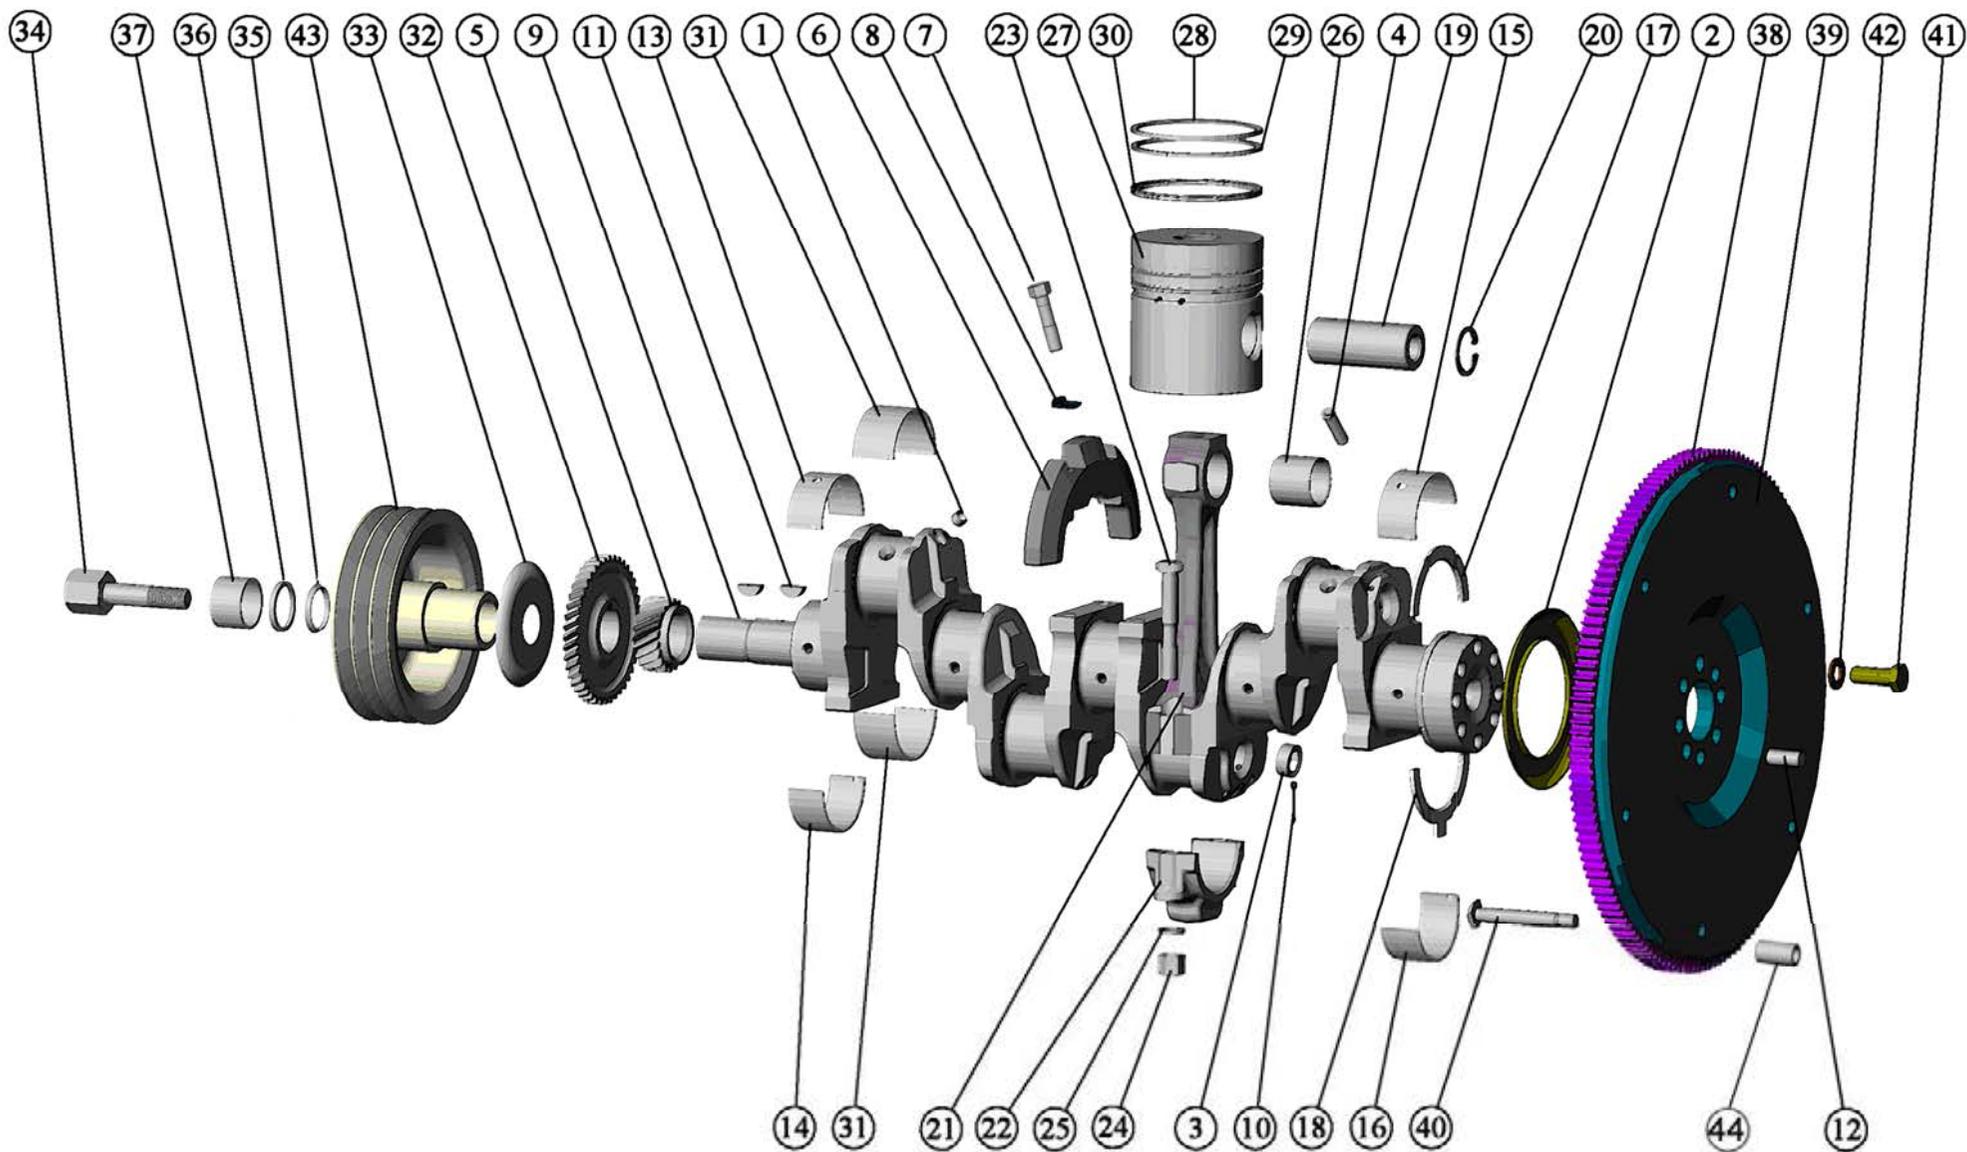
Поршни и шатуны. Коленчатый вал и маховик
